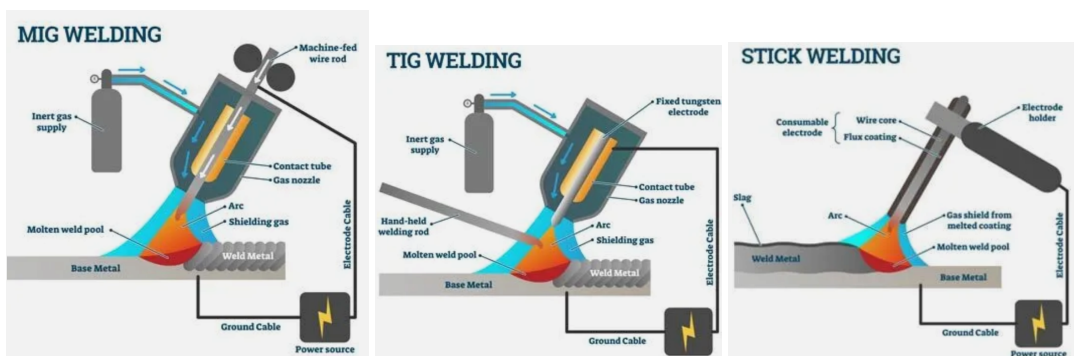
Tres tipos de soldadura por arco eléctrico
